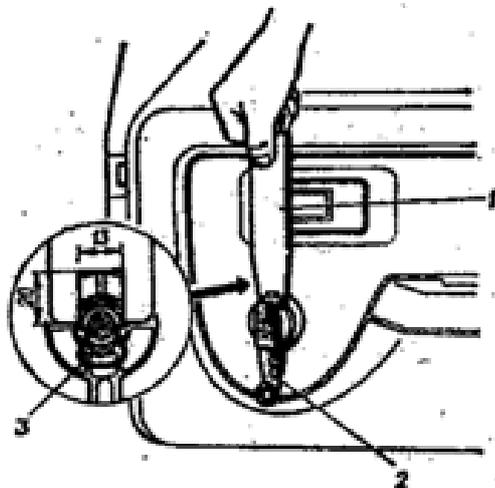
Снятие ручки привода стеклоподъемника: 1 - приспособление; 2 - ручка; 3 - пружина стопорная.
